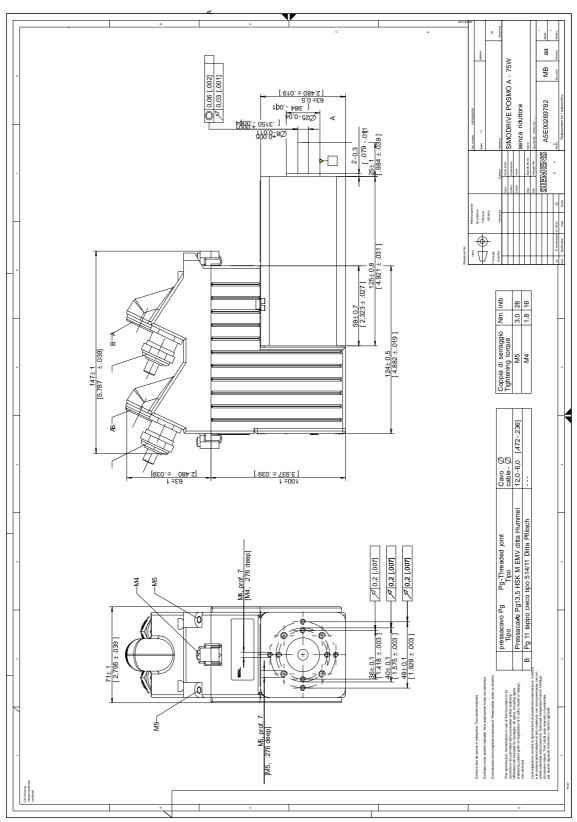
Dimensioni: SIMODRIVE POSMO A da 75 W senza riduttore
